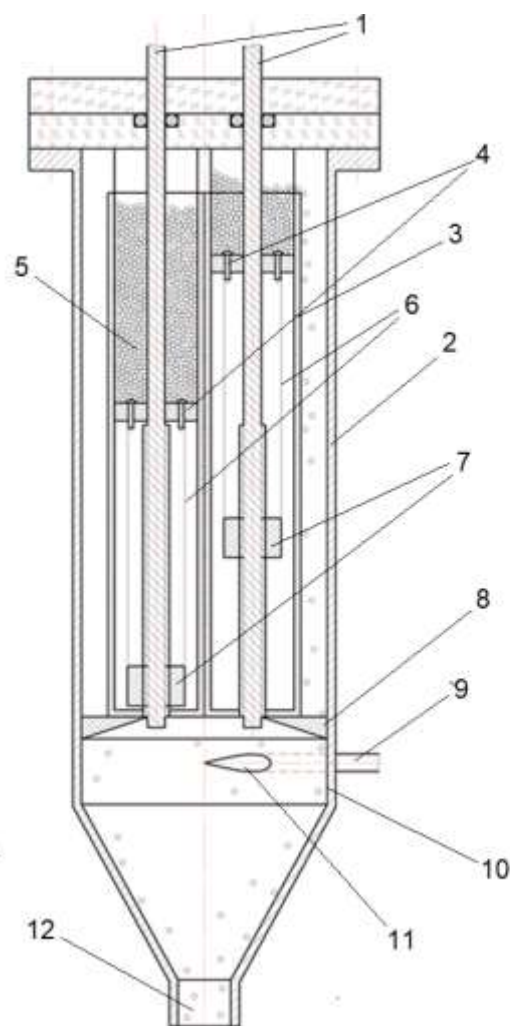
Схема порошкового питателя для плазменного напыления градиентного покрытия, содержащая 4 контейнера для порошков. 1 – валы питателя, 2 – внешний корпус, 3 – внутренний корпус, 4 – поршни, 5 – порошок, 6 – толкатели поршней, 7 – гайки толкателей поршней, 8 – упор внутреннего корпуса, 9 – трубка подачи несущего газа, 10 – камера выхода порошка из питателя, 11 – выходное отверстие трубки подачи несущего газа, 12 – выходное отверстие из питателя.
